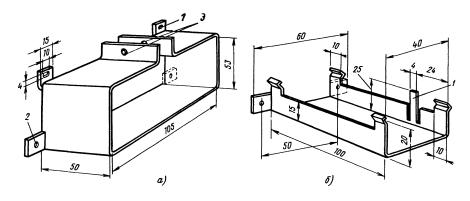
Конструкция кронштейнов крепления блоков СВП-3-1: a — для блока ПН-1; δ — для платы индикатора
